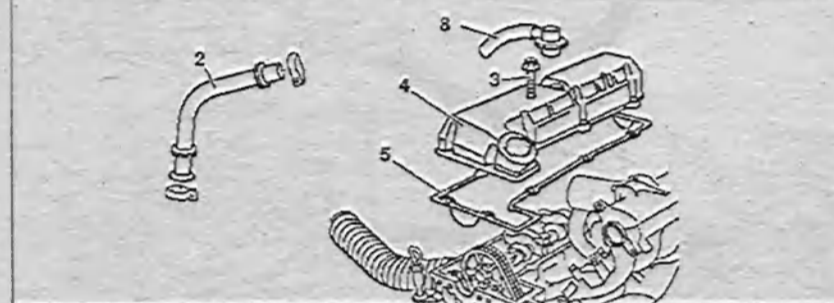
Крышка головки блока цилиндров двигателя 602.980:
